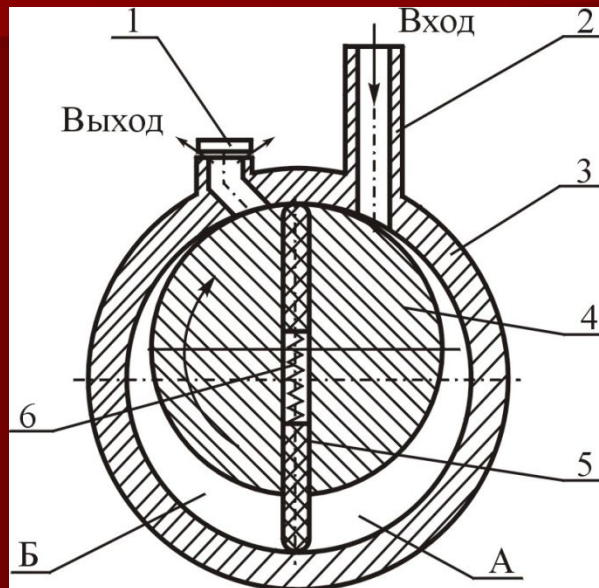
Схема механического (пластинчато-роторного) форвакуумного насоса: 1 – клапан выхлопной; 2 – патрубок входной; 3 – цилиндр; 4 – ротор; 5 – пластина; 6 – пружина
